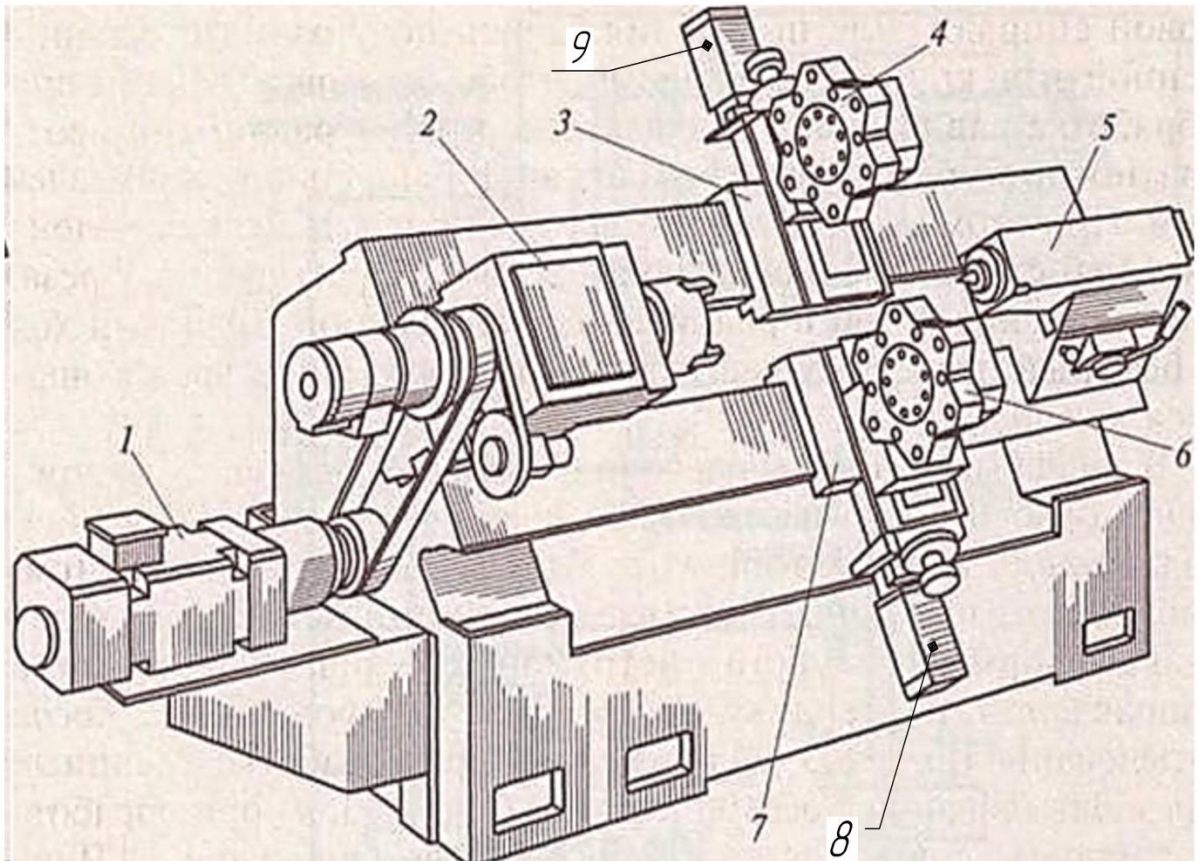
Токарно-револьверний верстат з ЧПК двохсупортний з попохилою станиною: 1 – двигун; 2 – шпиндельна бабка; 3 – верхній поздовжньо-поперечний супорт, 4 – револьверна головка верхнього супорта; 5 – задня бабка; 6 – револьверна головка нижнього супорта; 7 – нижній поздовжньо-поперечний супорт верстата [5]
